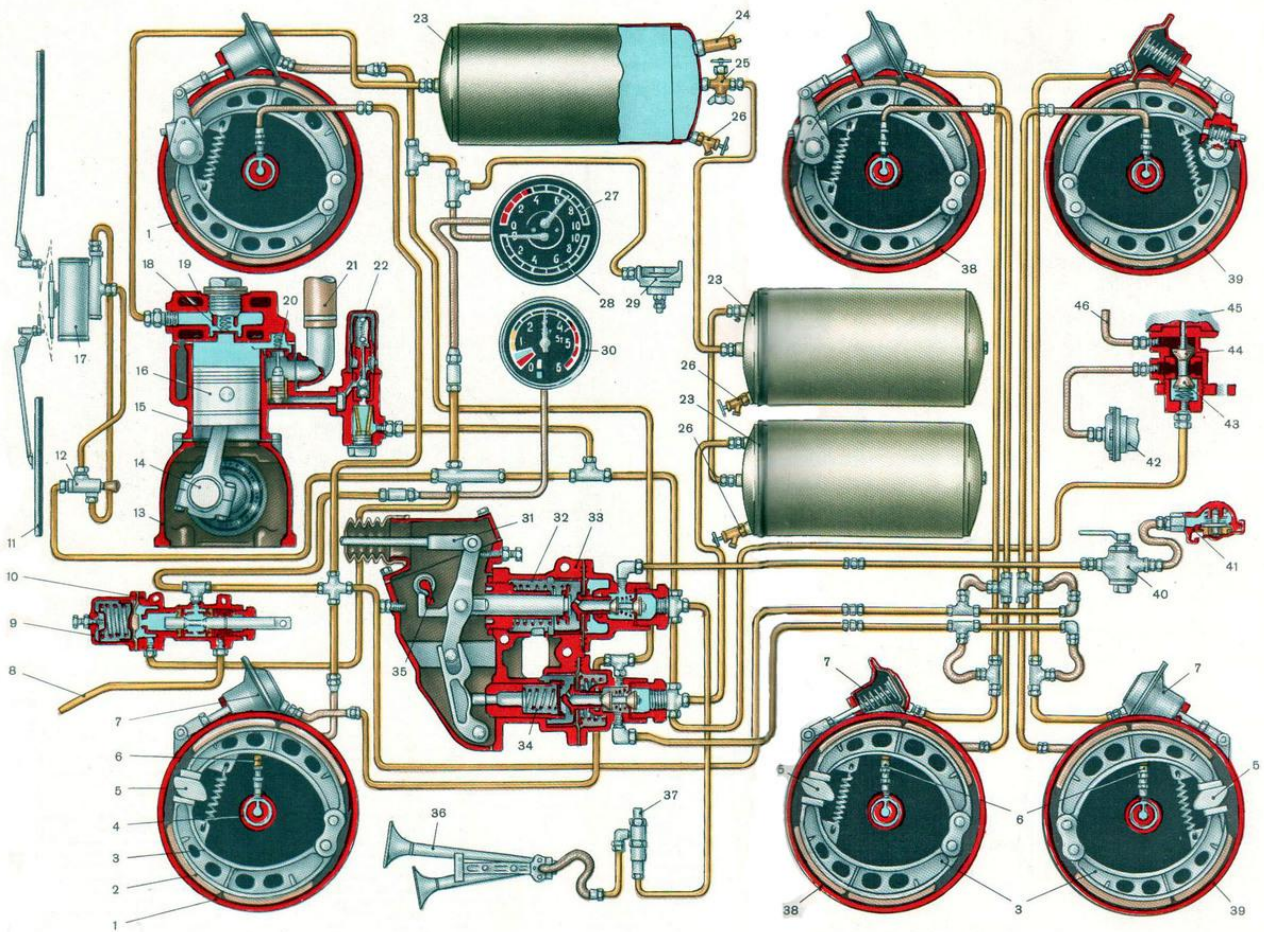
Схема пневматичного привода гальм і системи регулювання тиску повітря в шинах
